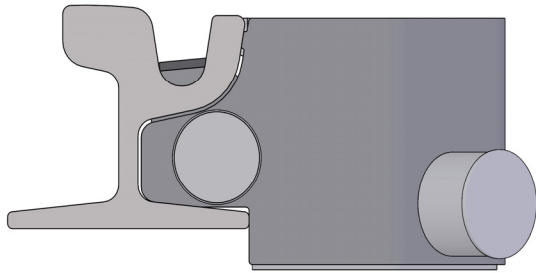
Type SK420-009 (Schienenprofile 53Ri1, Ri53-13, Ri53N; geschweißt)
